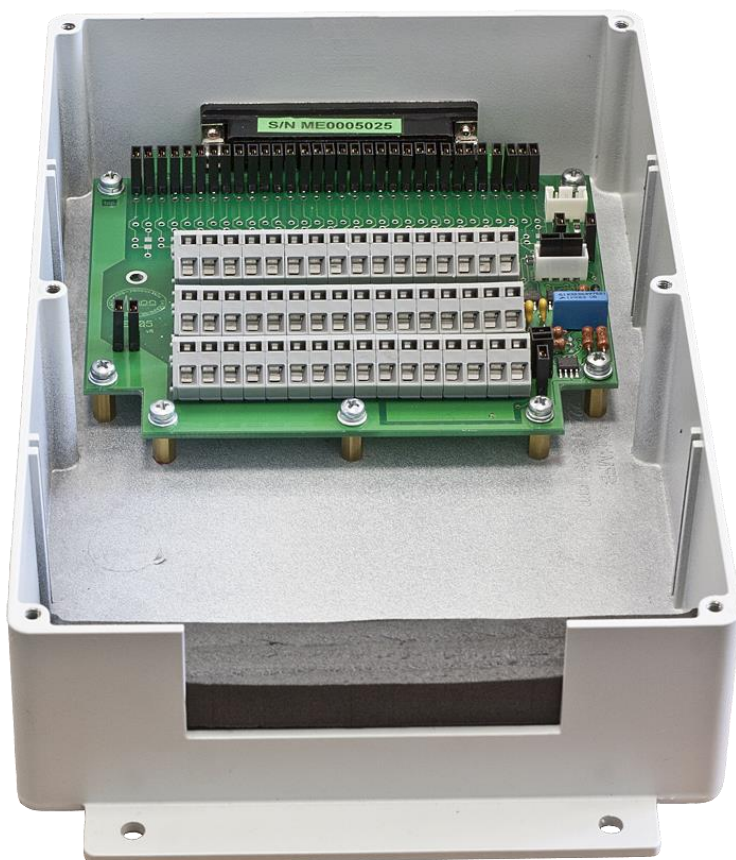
Общий вид модуля в корпусе со снятой крышкой
